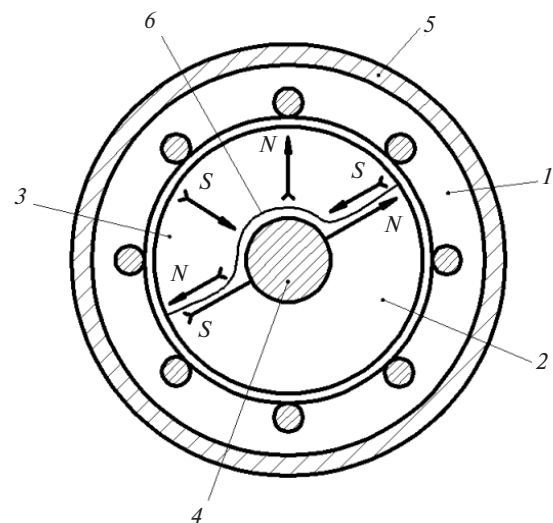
Поперечное сечение синхронного генератора: 1 – якорь (магнитопровод с якорной обмоткой); 2 – основной индуктор; 3 – дополнительный индуктор; 4 – вал; 5 – наружный корпус; 6 – линия вырыва
